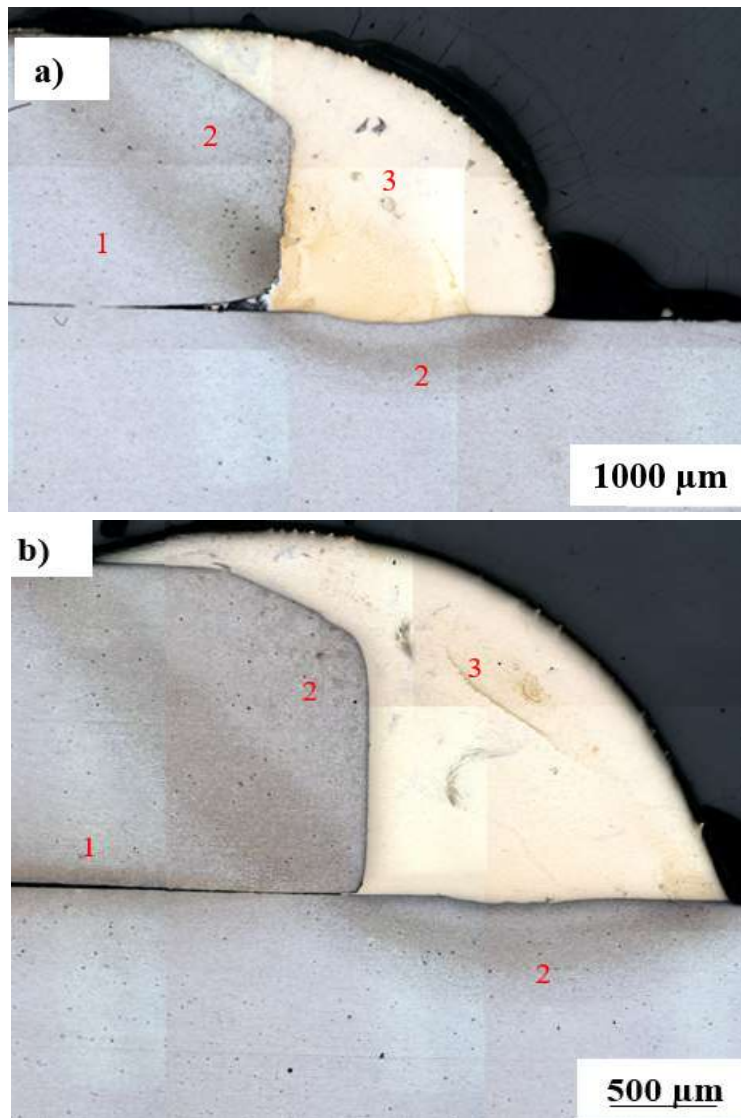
Macrografías de las uniones soldada con el electrodo ERCuAl-A2 mediante el proceso de soldadura GMAW-P Brazing, tomadas con MO a 5x, a) C1-B b) C2-B.
